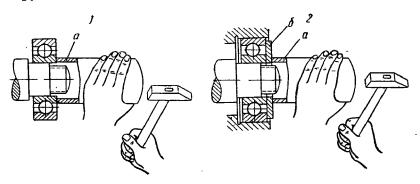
Насадка шариковых подшинников на шейки вала и в корпус: 1 — на шейку вала с помощью отрезка трубы а; 2 — на шейку вала в корпус с натягом при помощи отрезка трубы а и подкладки б.
